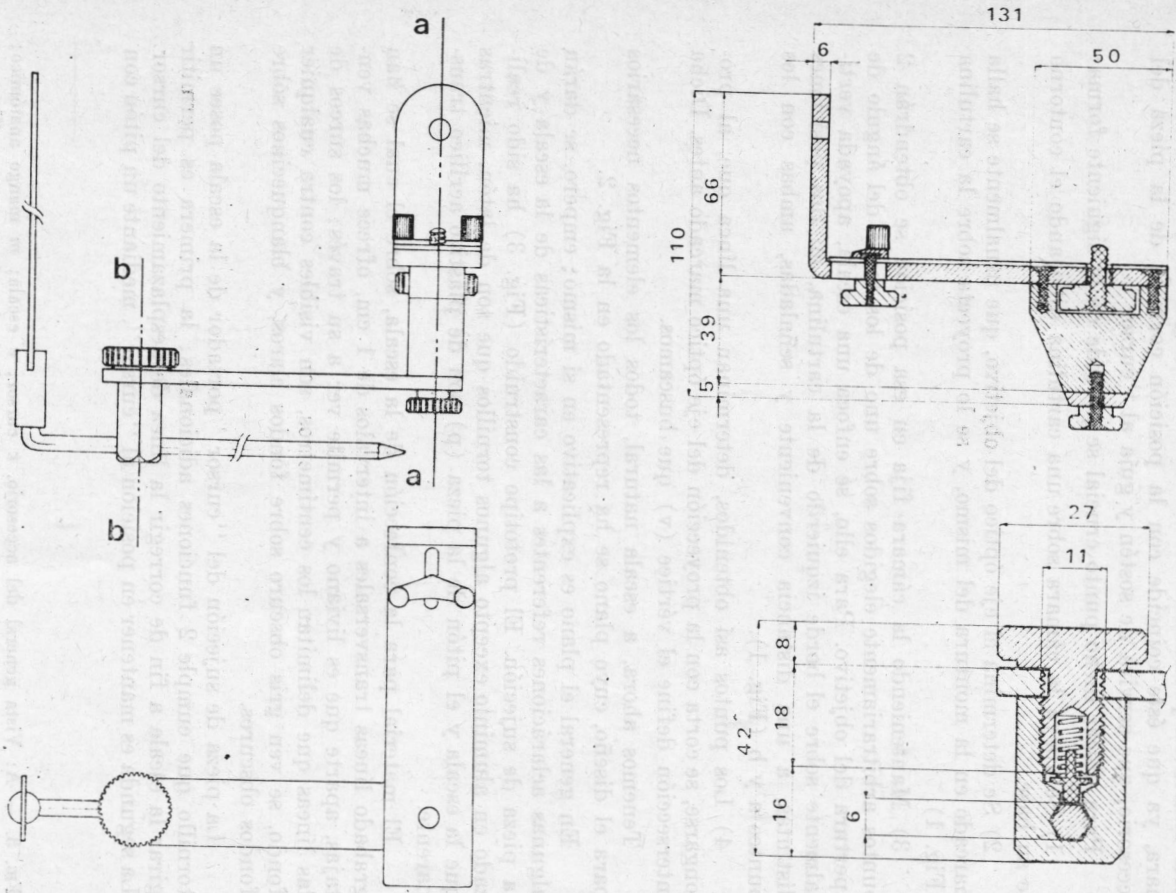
Plano del accesorio. Arriba a la izquierda, vista lateral; arriba a la derecha, vista frontal en corte por el plano *aa*; abajo a la izquierda, vista superior; abajo a la derecha, detalle de la pieza *p* por plano de corte *bb*. Todas las medidas en milímetros.
